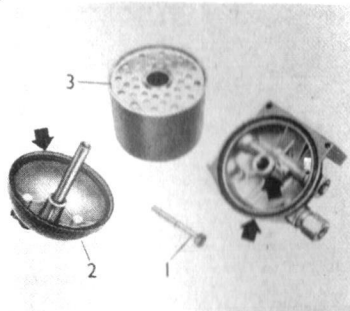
Vista esplosa filtro carburante (mot. 2524 cc.).
